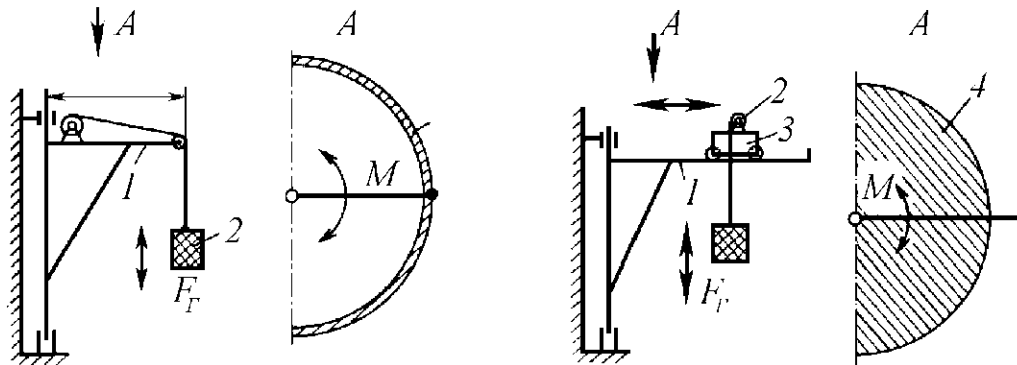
Схемы настенных консольных поворотных кранов
